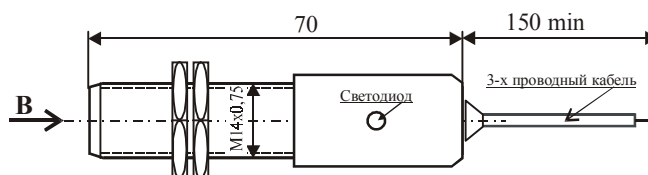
Внешний вид и габаритные размеры датчиков типа
